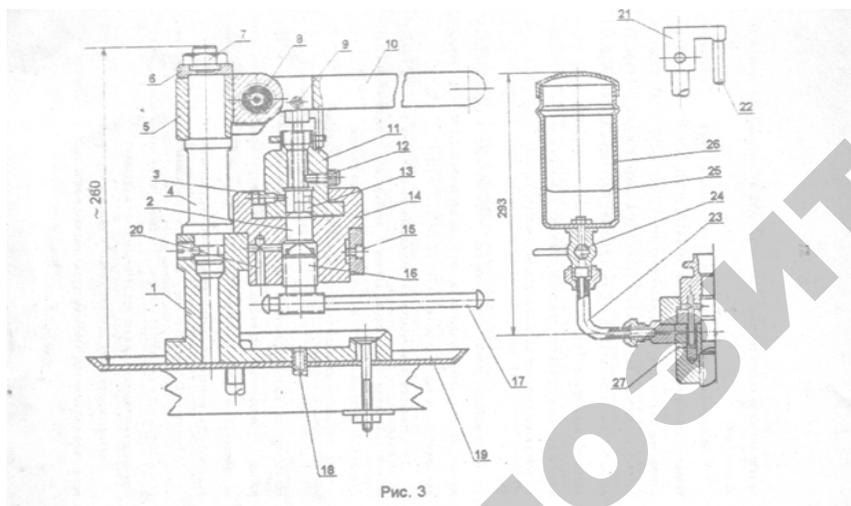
Устройство прибора для испытания плунжерных пар
